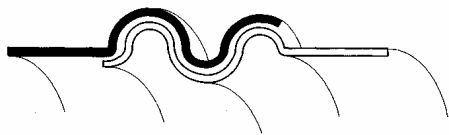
Фальцевое соединение круглых элементов на зиге
